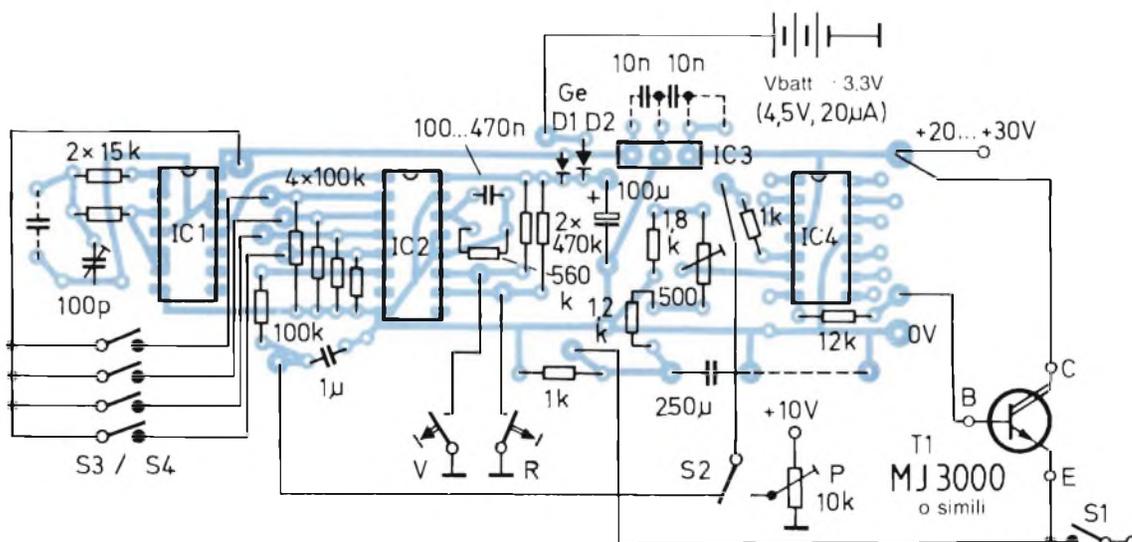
Disposizione dei componenti e dei collegamenti cablati.
